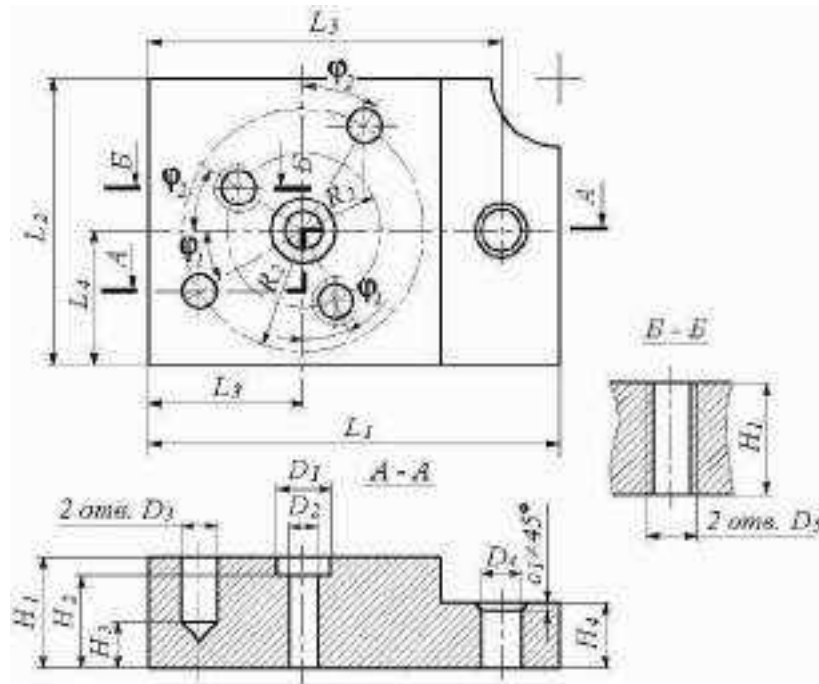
Эскиз обрабатываемой детали для вариантов 3, 8, 13, 18, 23
